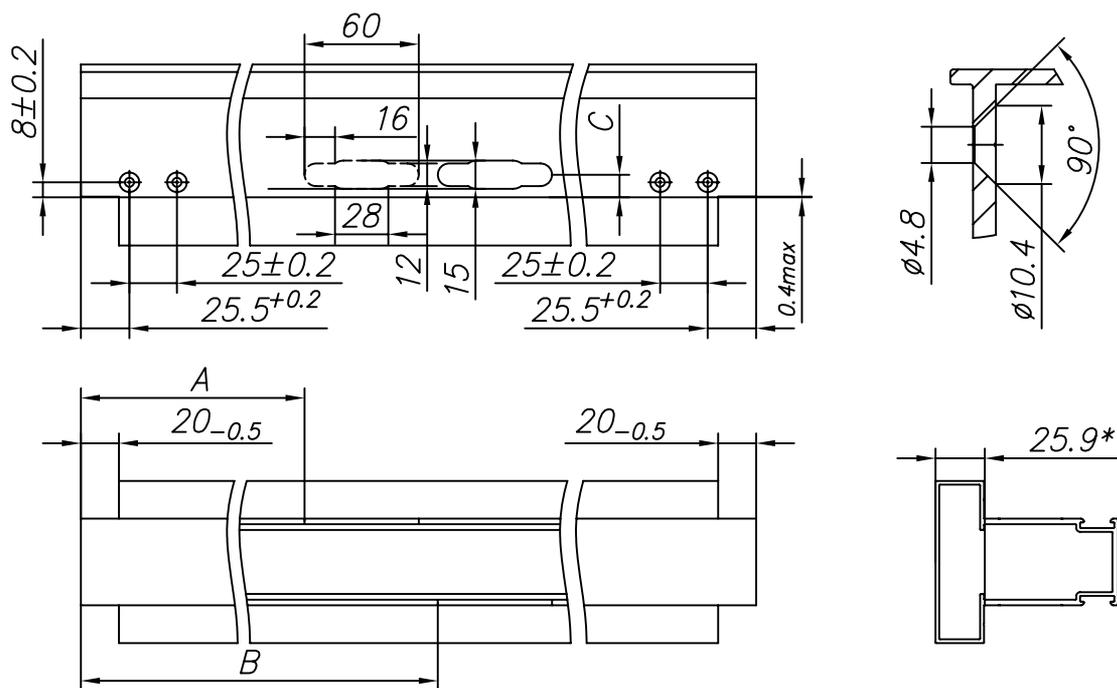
Изготовление импоста с пазами для тросовой растяжки
